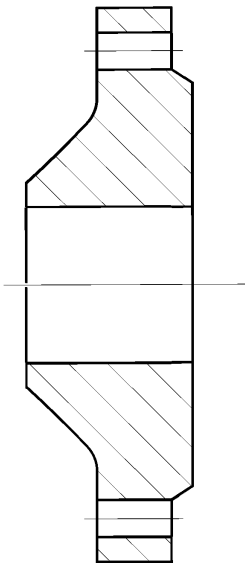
Конструкции фланцев стальных приварных встык
